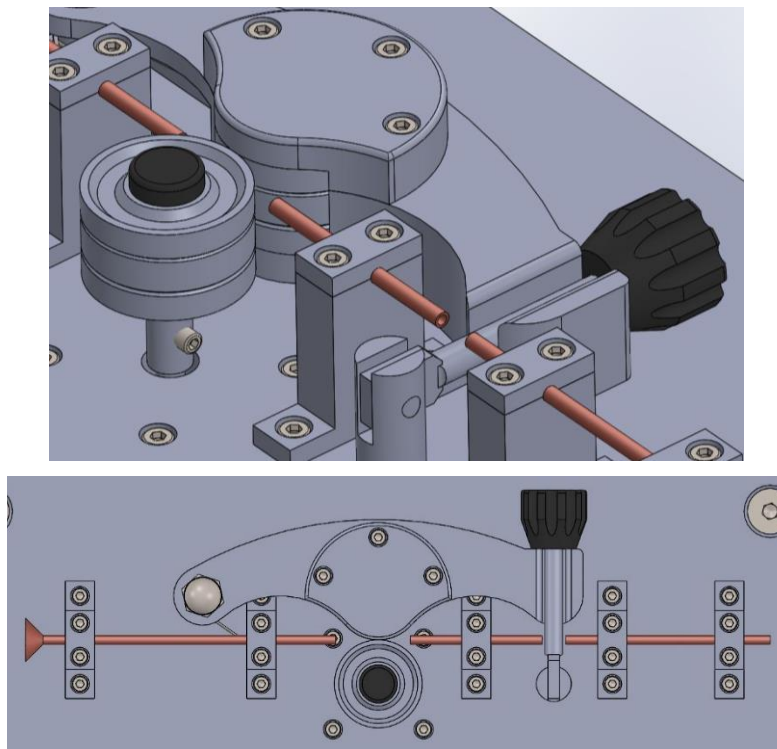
Vista CAD detallada de las roldanas y vista CAD superior del mecanismo del alimentador del hilo.
